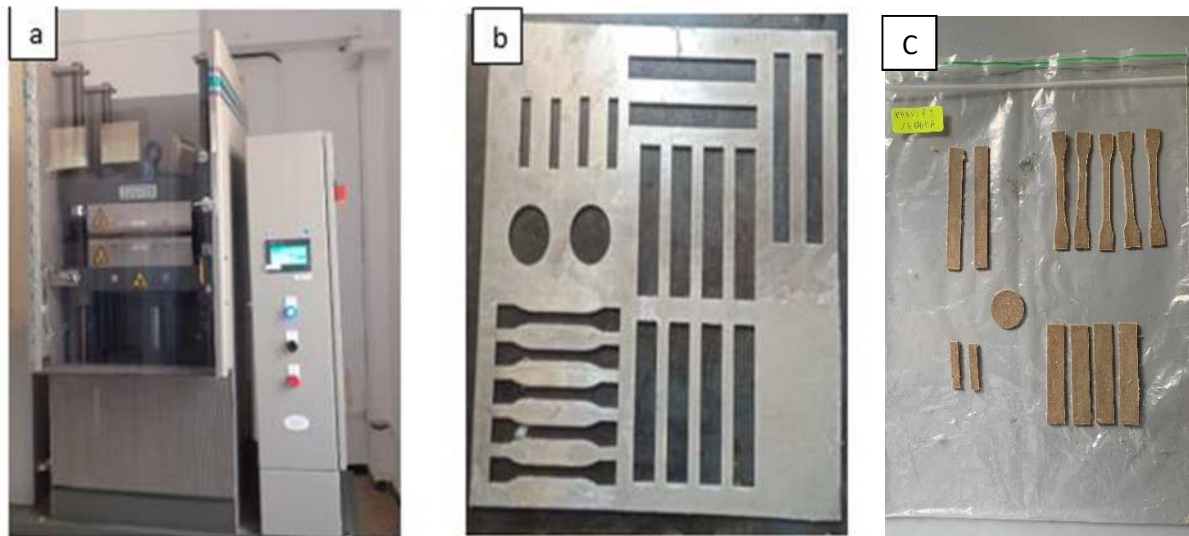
a) Presse hydraulique de marque CARVER, b) le moule des éprouvettes, c) éprouvettes
